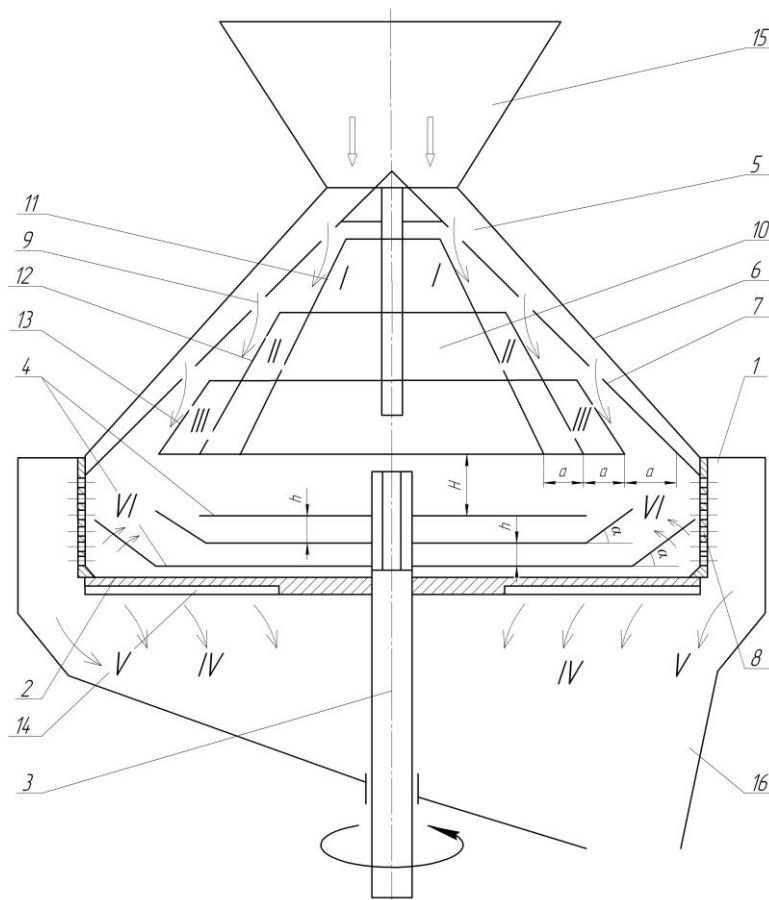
Схема робочої камери дробарки зерна прямого удару.
